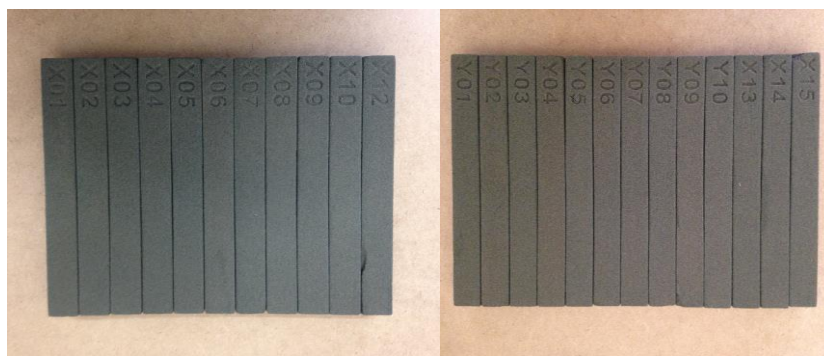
Eprouvettes en sable imprimées avec le procédé résine furanique
